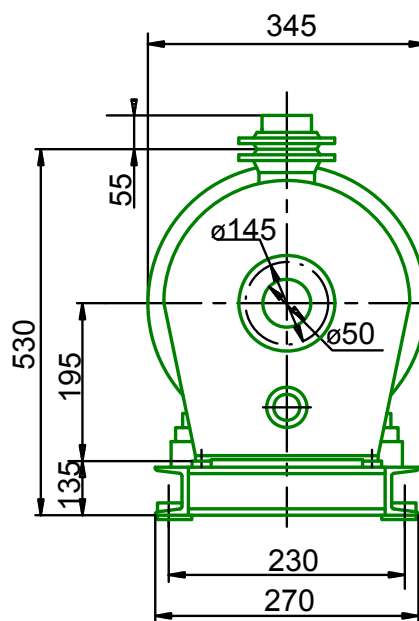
Габаритный чертеж насосного агрегата типа ЦНА 12,5/50
